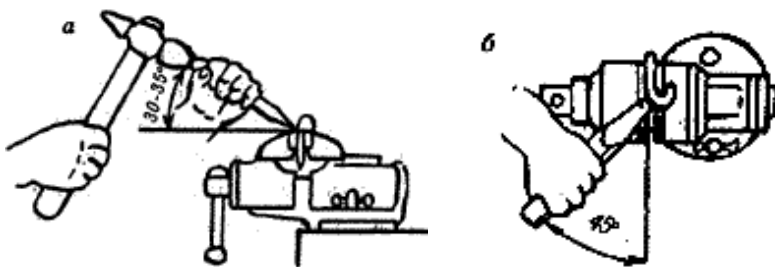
Рубка зубилом: а – вид сбоку; б – вид сверху
